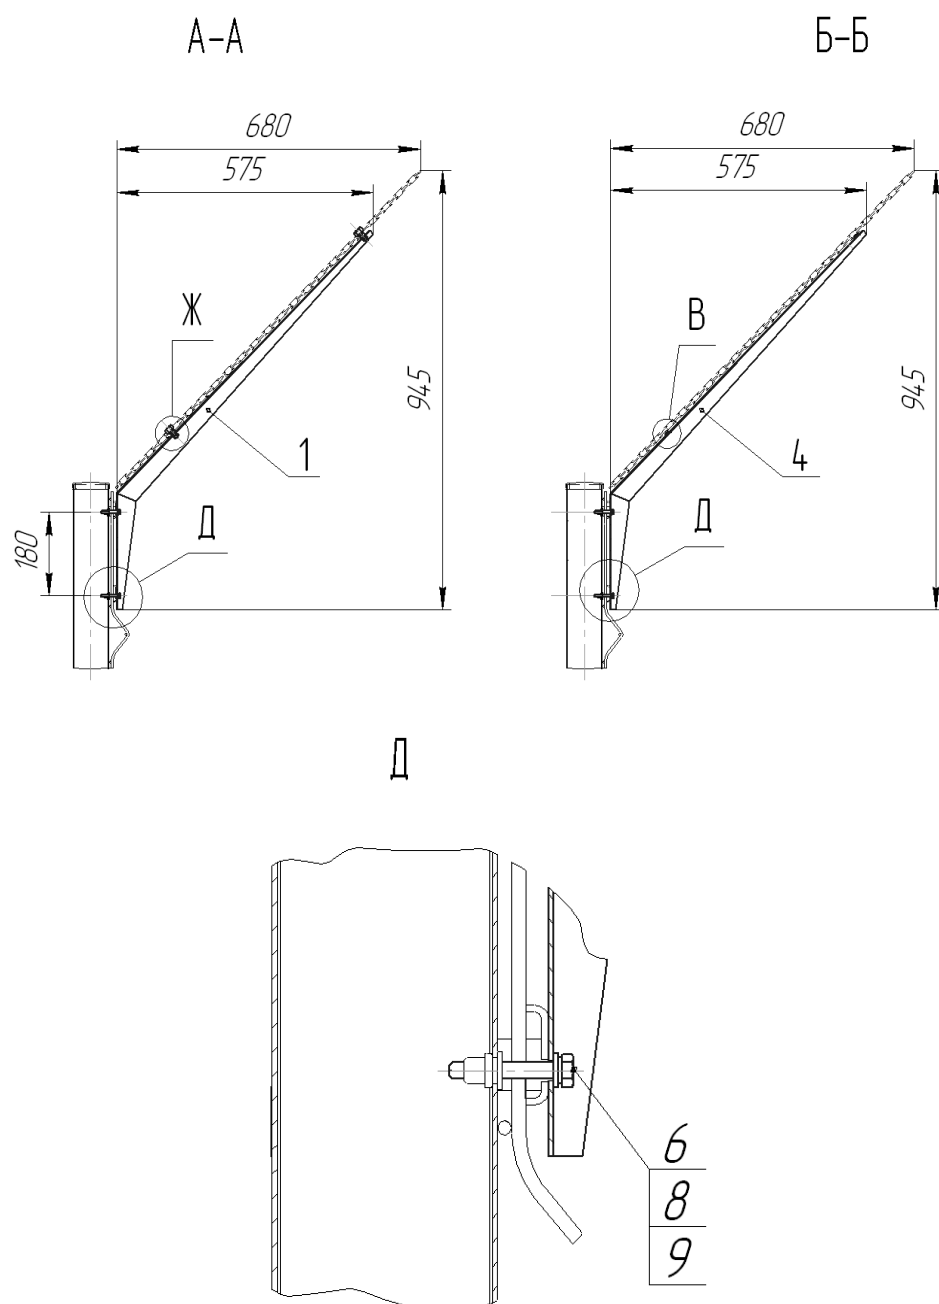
Разрезы А-А, Б-Б, детальный вид Д
